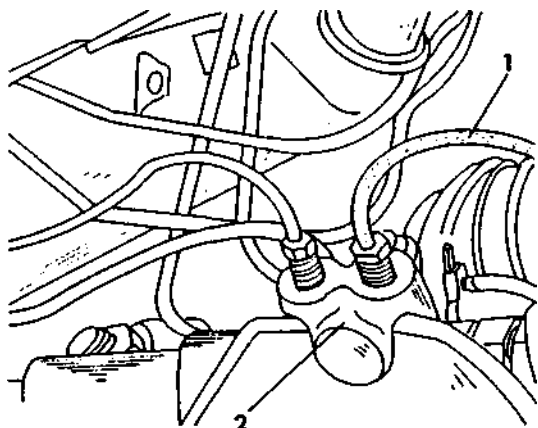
Vypouštěcí šroub -1- a tlakové vedení -2- na tlakovém regulátoru
